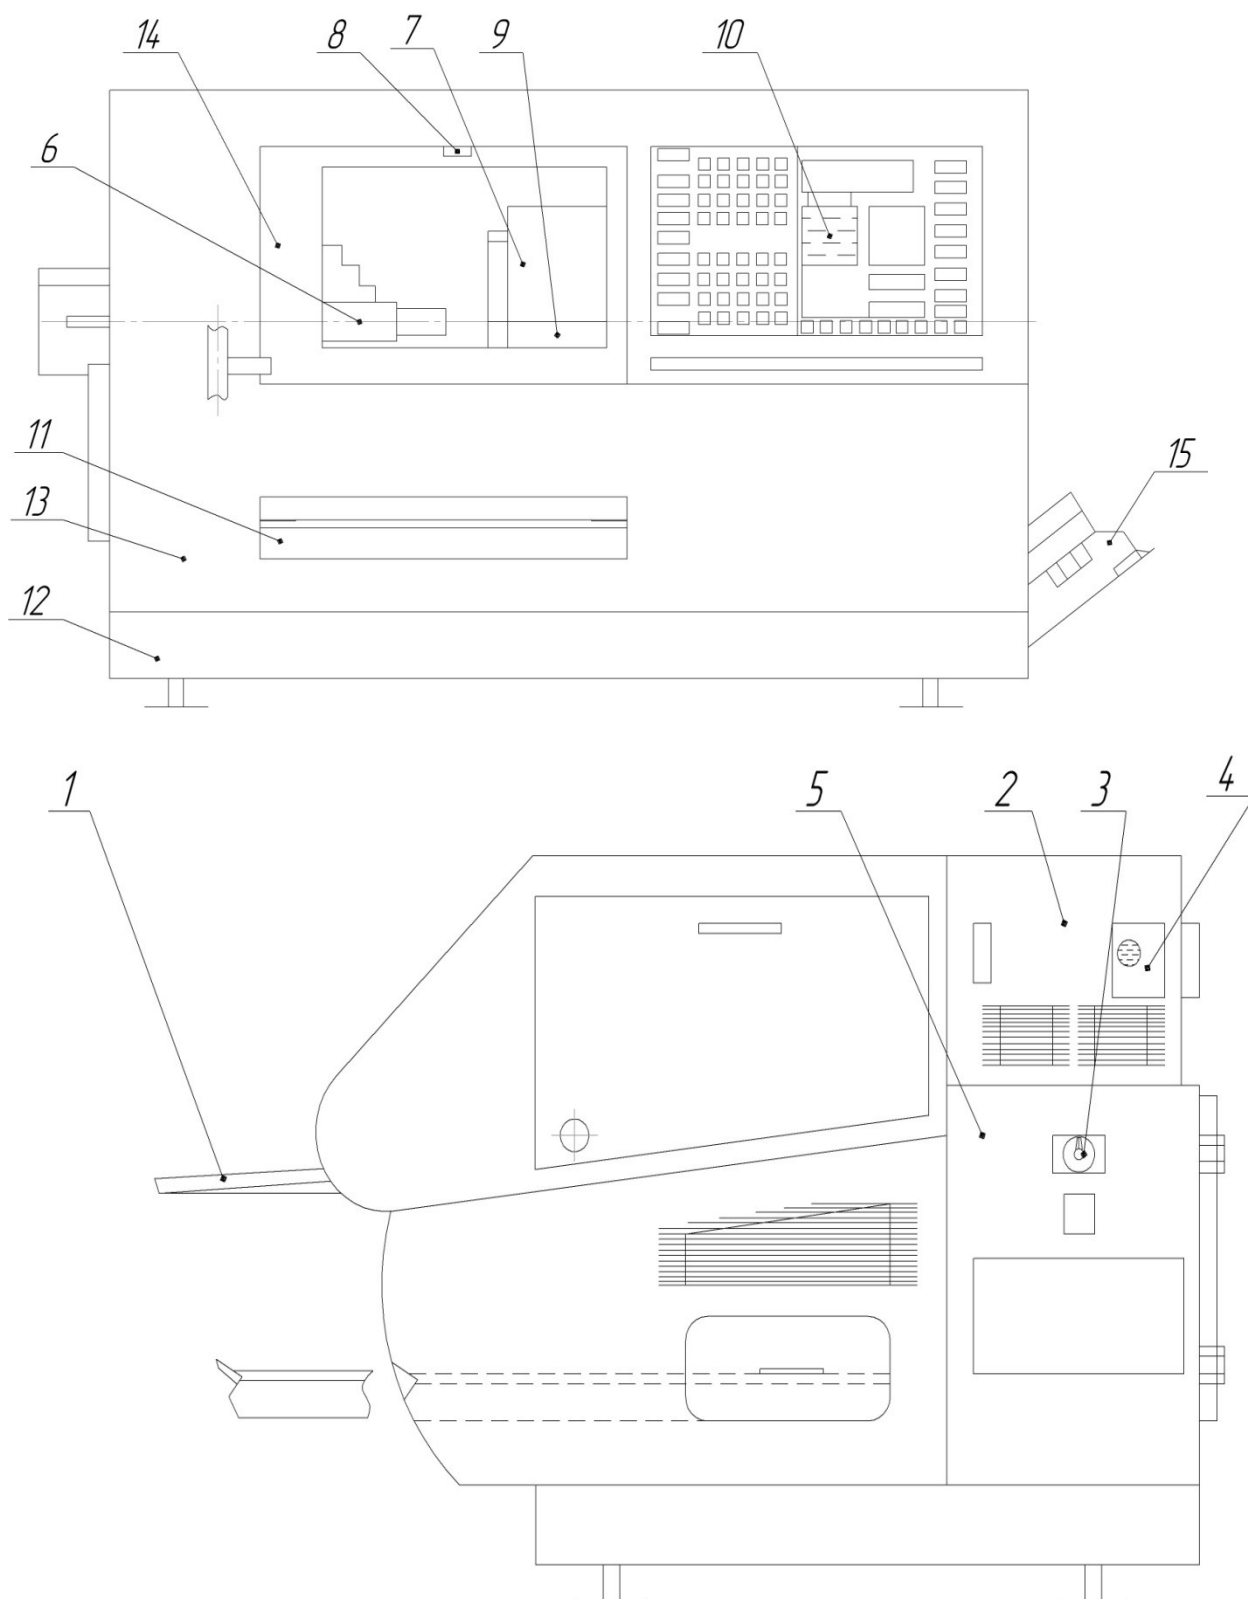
Основные элементы токарно-фрезерного станка EMCO CONCEPT TURN 155.
